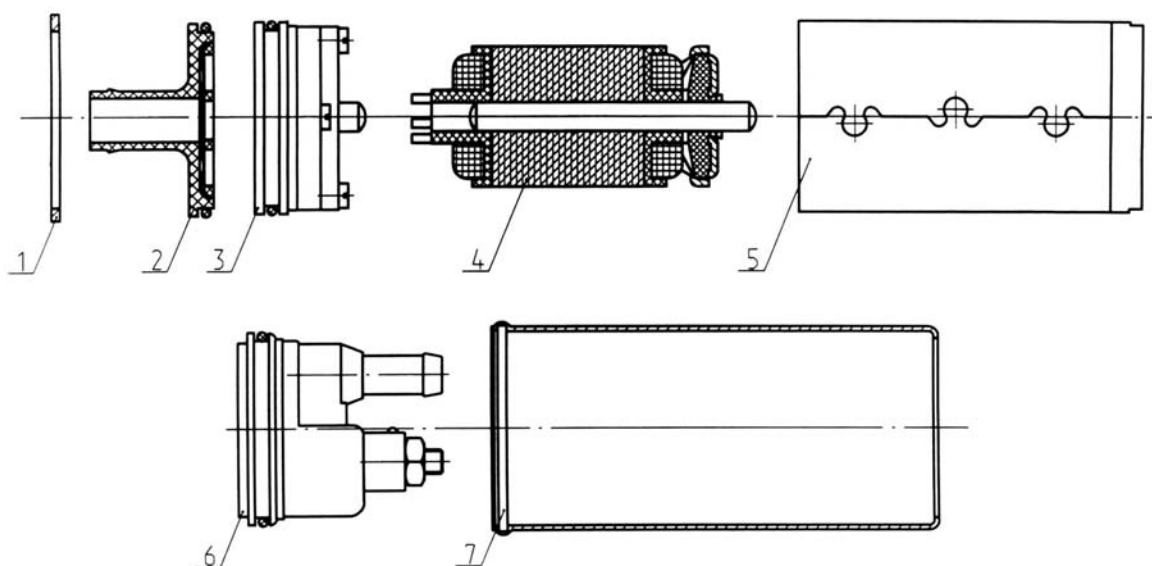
Порядок разборки и сборки деталей и сборочных единиц ЭБН: 1 – стопорное кольцо; 2 – входная крышка; 3 – насос; 4 – якорь; 5 – статор электропривода; 6 – выходная крышка; 7 – корпус ЭБН
